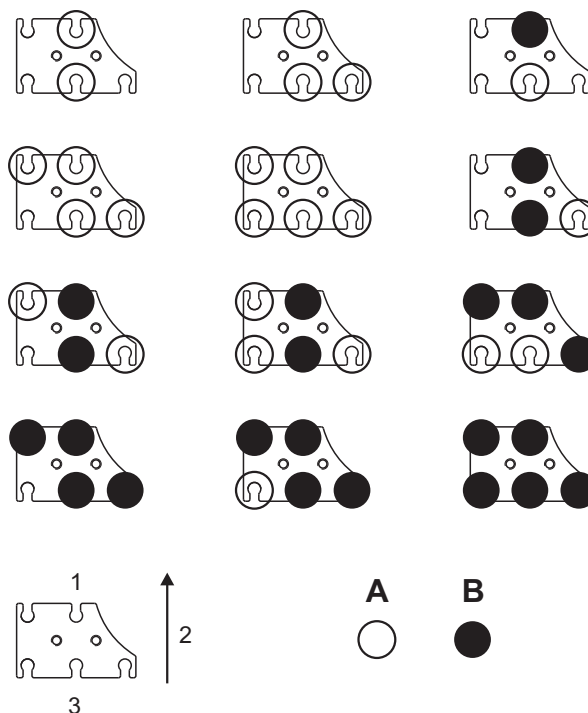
Utrustningsplan utjevningsfjær Access XL
